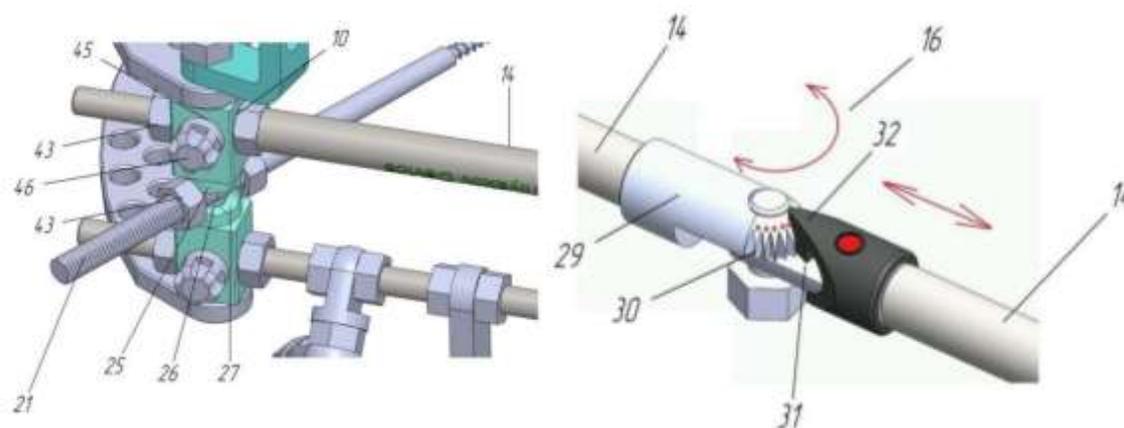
Общий вид балки и вид одноосевого шарнира с зубчатым фиксатором
